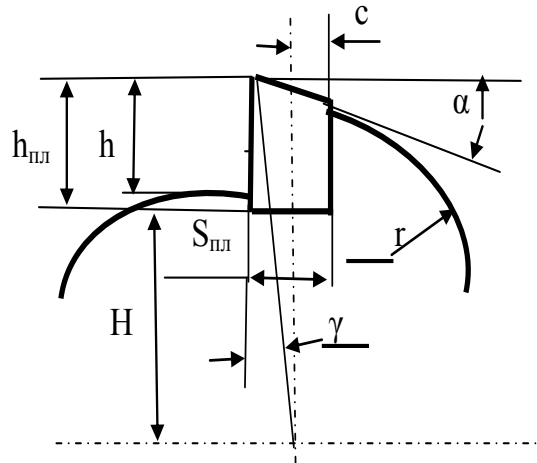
Профиль торцового сечения фрез с напайными пластинками по стандартам:
